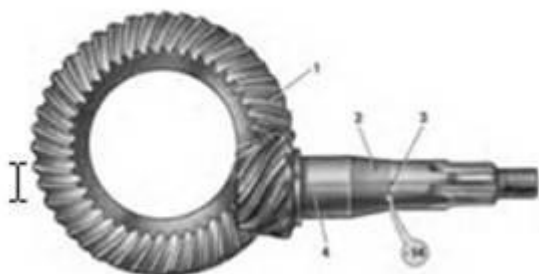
Шестерни главной передачи: 1 — ведомая шестерня; 2 — порядковый номер; 3 — поправка в сотых долях миллиметра к номинальному положению; 4 — ведущая шестерня.
